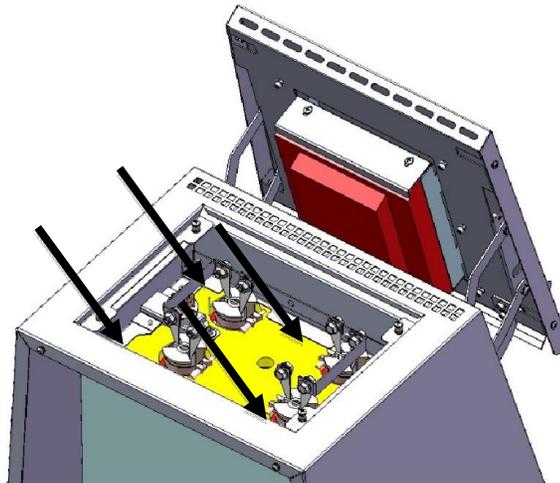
Hastes de aquecimento fixadas, topo do forno
